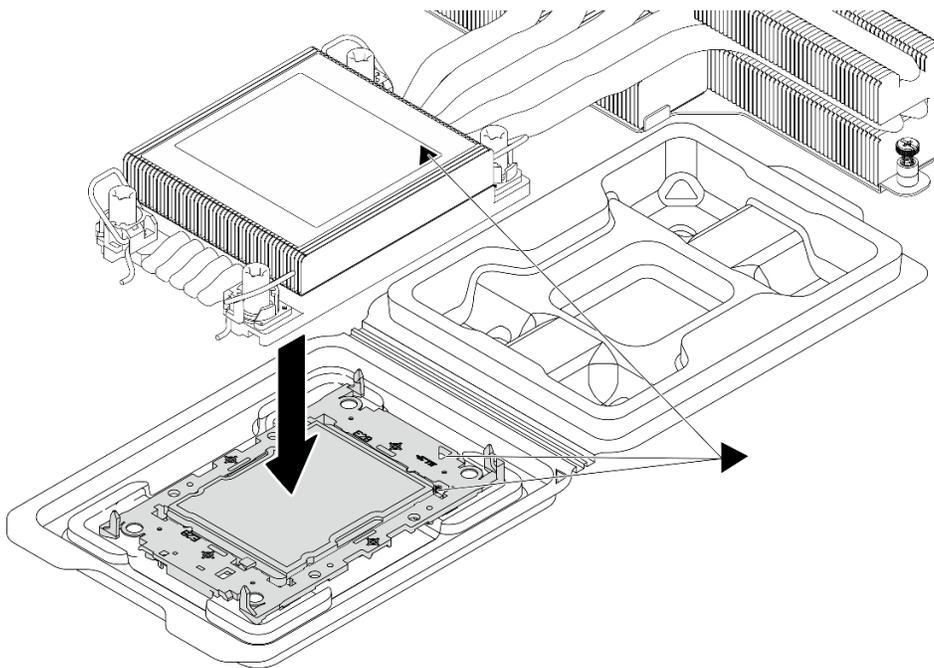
Assemblage du module de processeur-dissipateur thermique avec le processeur dans le plateau d'expédition
